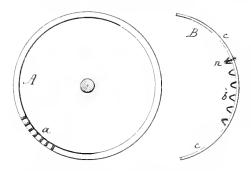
Coupes de décrotteurs de betteroves. A. Machine Billy. — B. Machine Lanne.
